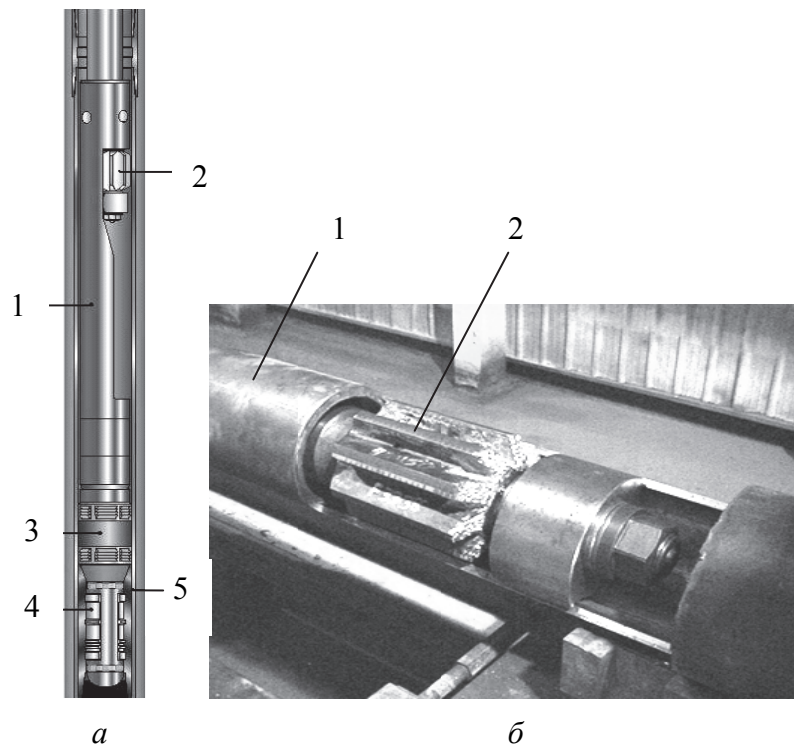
Скважинный фрезерный станок: а – схема станка; б – вид станка со стороны фрезы 2: 1 – корпус; 2 – фреза; 3 – якорный паккер; 4 – фиксатор
